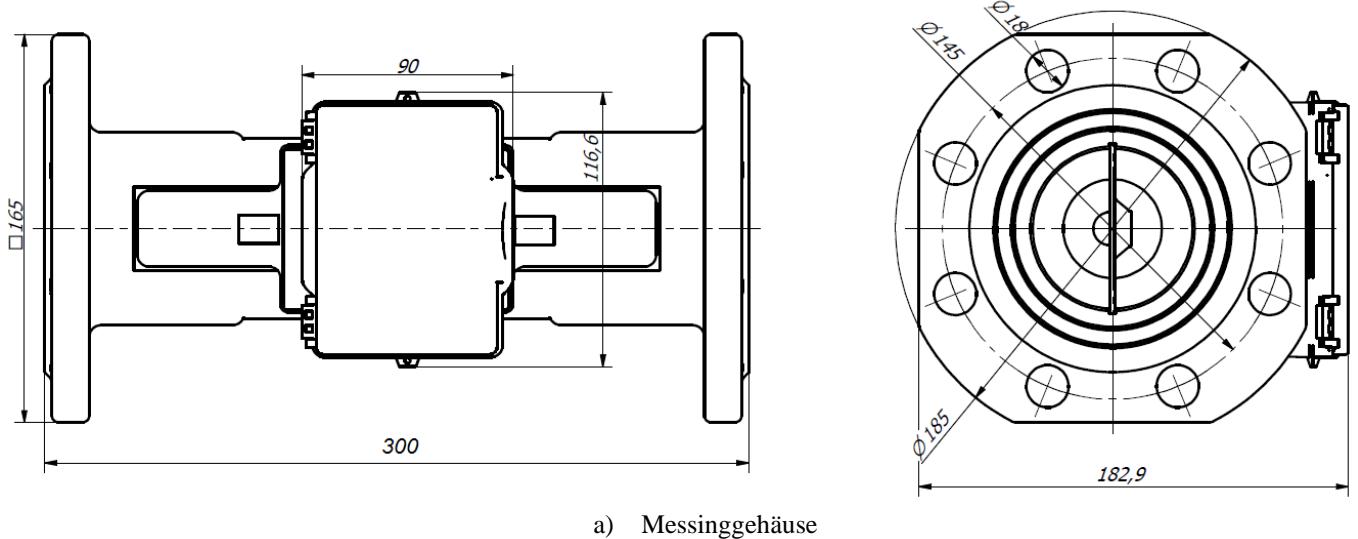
Flanschanschlüsse DN65, Baulänge L=300 mm
